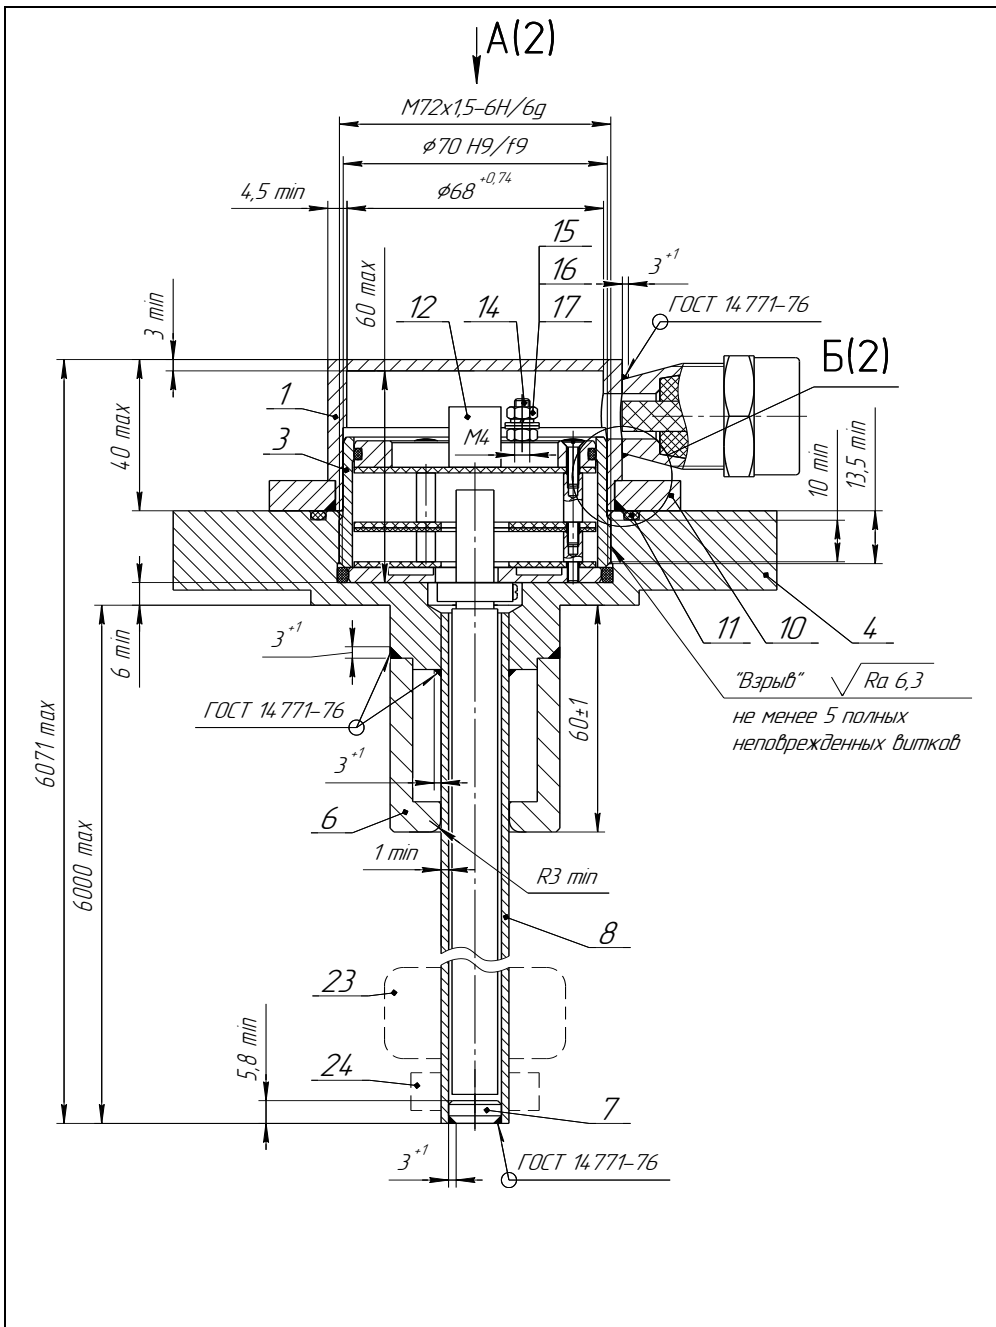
(лист 1 из 4) – Чертеж средств взрывозащиты варианта со сварным корпусом из нержавеющей стали (НЖ)
